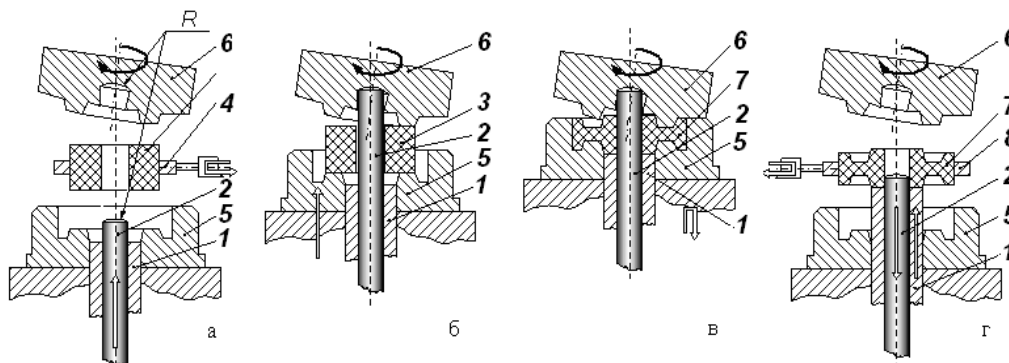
Этапы протекания технологического процесса с использованием кольцевой заготовки: а – подача заготовки в рабочую зону; б – начало ШСО; в – конечная стадия ШСО; г – удаление детали из рабочей зоны
